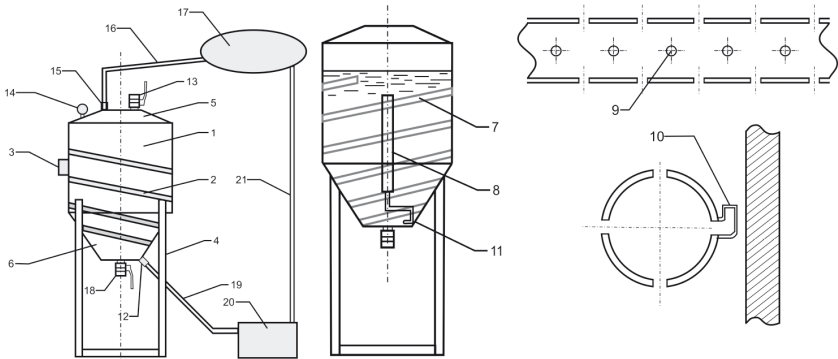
Общий вид предлагаемой биогазовой установки, общий вид барботажного перемешивающего устройства, перфорированная барботажная труба в разрезе. 1 – цилиндрический резервуар, 2 – нагревательная лента, 3 - терморегулятор, 4 - опоры, 5 – купол, 6 – днище, 7 – спиралевидная перфорированная труба, 8 - вертикальная перфорированная труба, 9 – отверстия спиралевидной и вертикальной труб, 10 – насадки в виде уголка, 11 – стальной цилиндрический уголок, 12 – шаровый кран, 13 – загрузочный патрубок, 14 – датчик давления, 15 – патрубок для выхода биогаза, 16 - газовый трубопровод, 17 - газгольдер, 18 – патрубок для выгрузки переработанного субстрата, 19 – газовый трубопровод, 20 - компрессор, 21 – газовый трубопровод.
